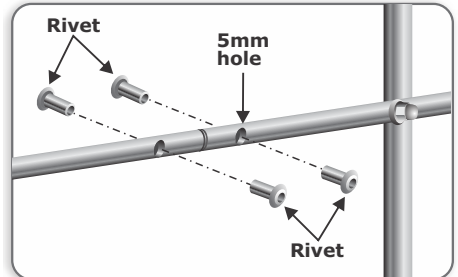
RIVETER LES BARRES TRANSVERSALES SUR LE RACCORD DE LA BARRE TRANSVERSALE
